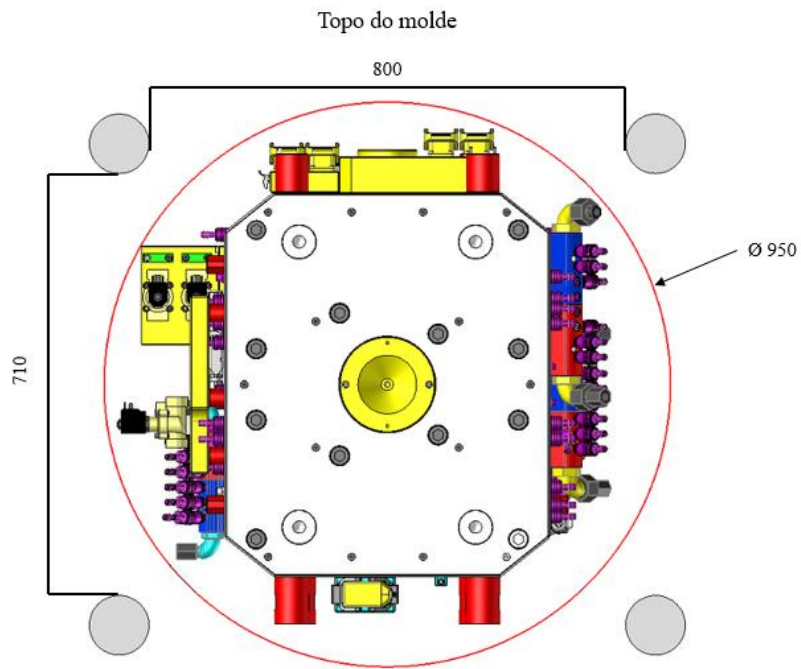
Planta do molde com o diâmetro útil do prato rotativo e colunas da máquina de injeção.
